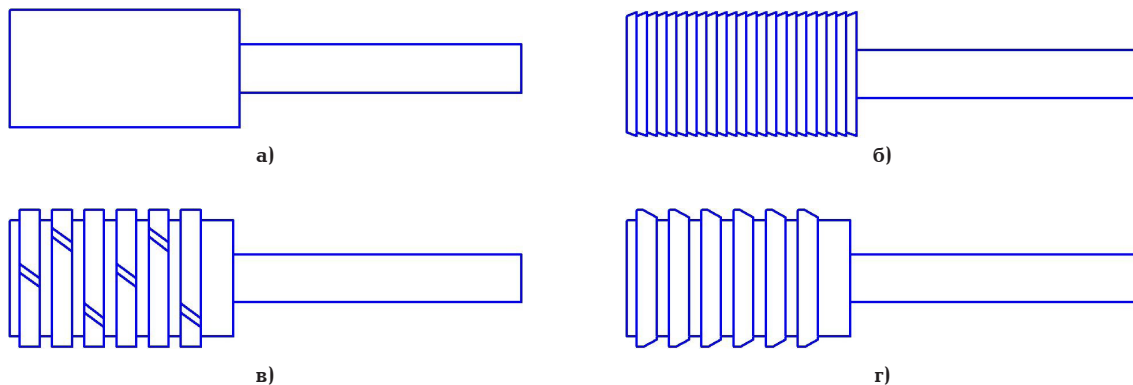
Схемы существующих типов цилиндропоршневых уплотнений компрессорных агрегатов:
